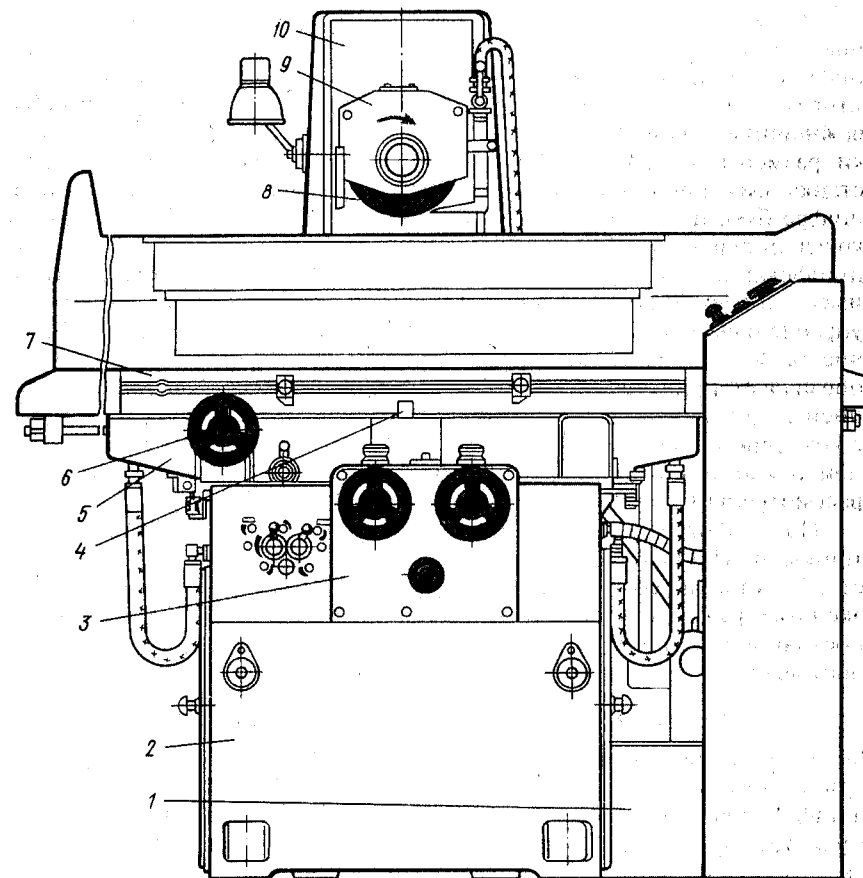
Общий вид плоскошлифовального станка с горизонтальным шпинделем и прямоугольным столом
